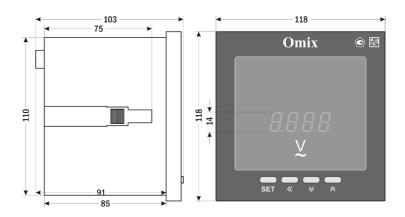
Размеры. Тип корпуса Р1212
